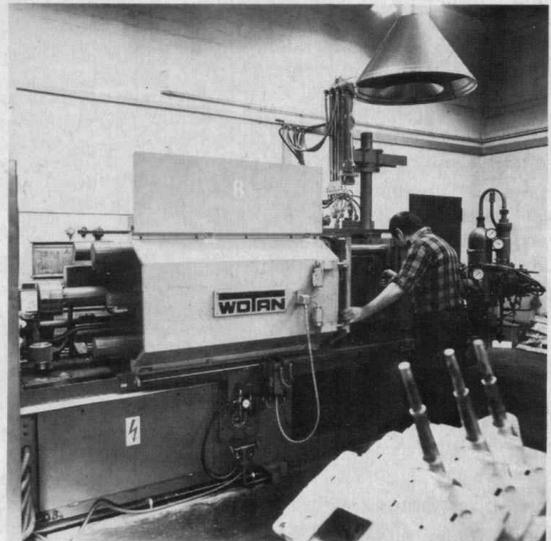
Kaltkammermaschine mit horizontalem Preßkolben
